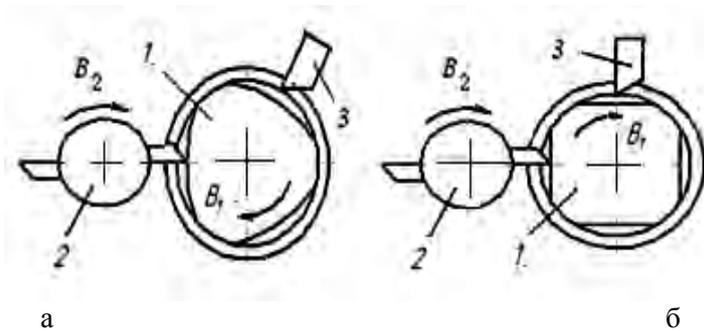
Рациональные схемы относительного расположения резца и резцовой головки при совмещенной обработке круглой поверхности и поверхности с тремя (а) и четырьмя (б) гранями
